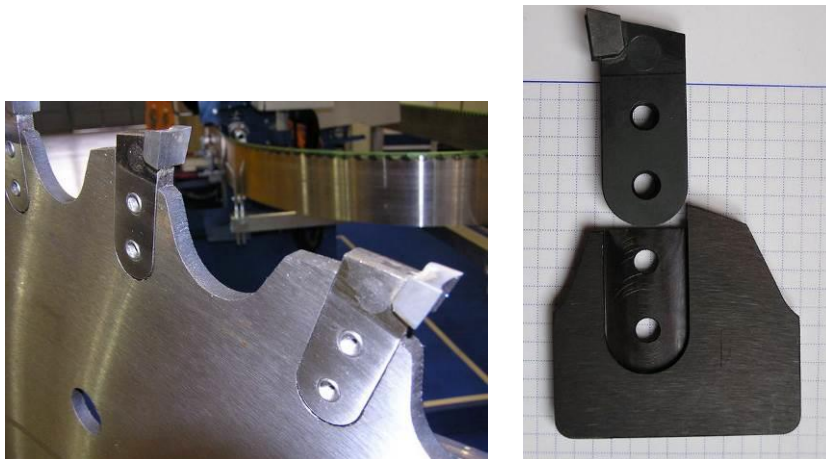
Moderní pilový kotouč s SK plátky (www.fachshop.cz)
